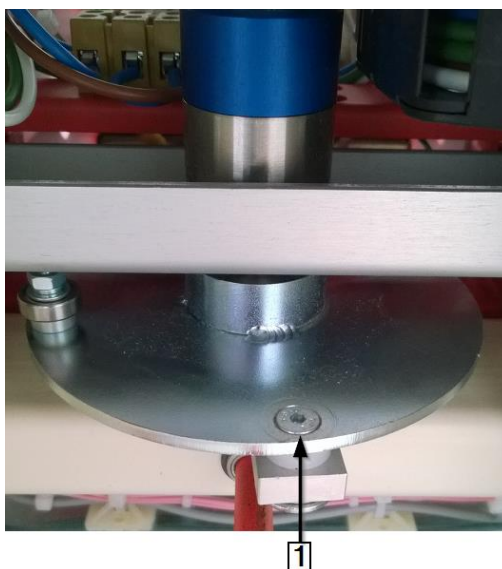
Tylny czop skrzętu tarczy mechanizmu korbowego silnika
